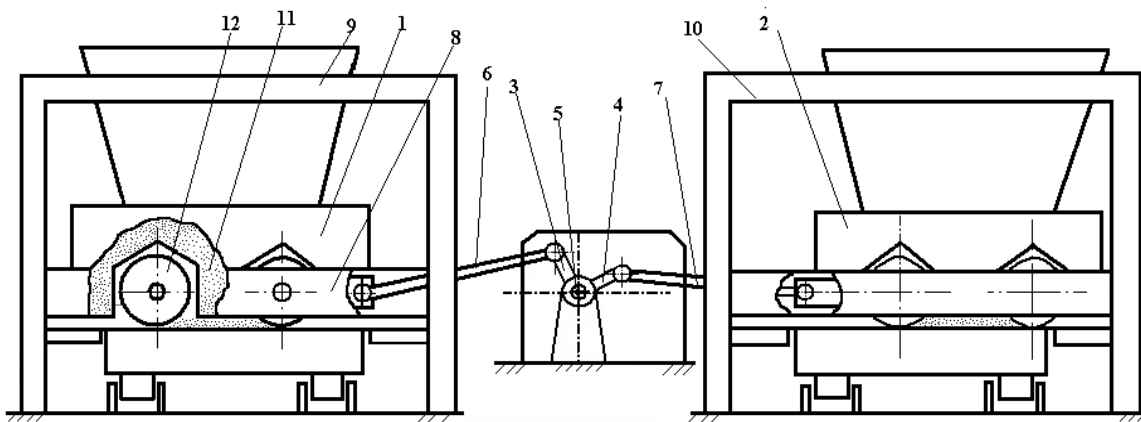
Роликова формувальна установка з рекупераційним приводом.
